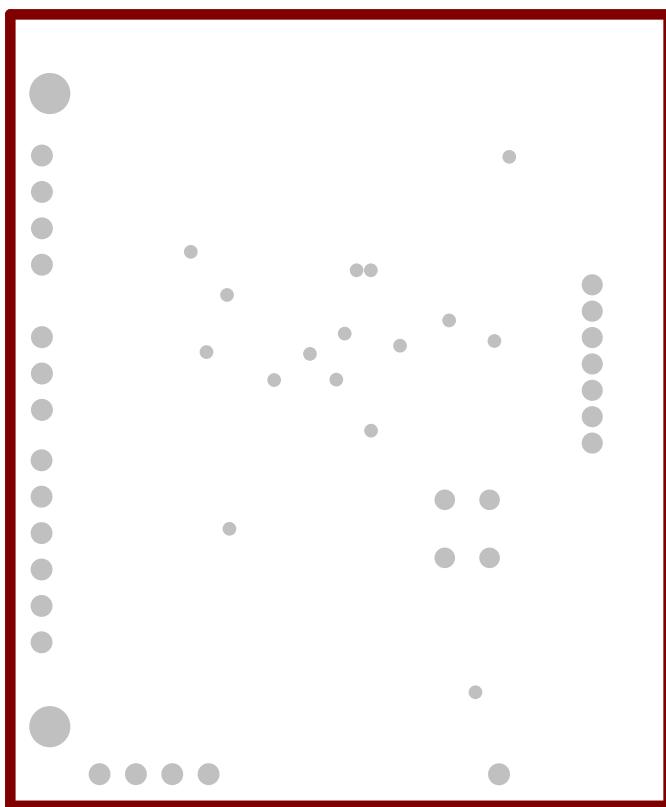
ADS124S18EVM の PCB レイアウト — 内部グランド (GND) 層 2
